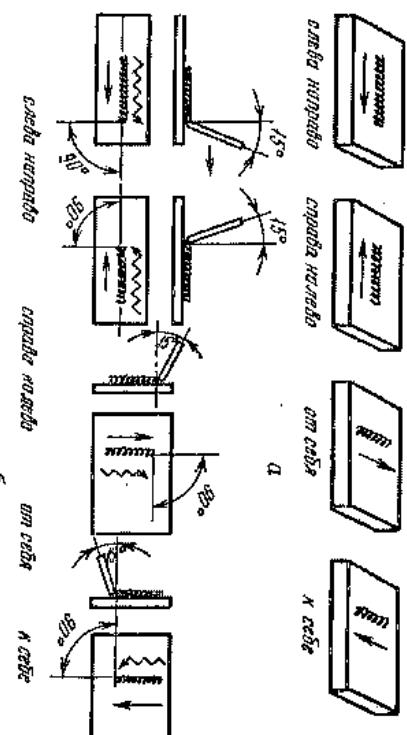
Направления сварки (а) и наклон электрода (б)
